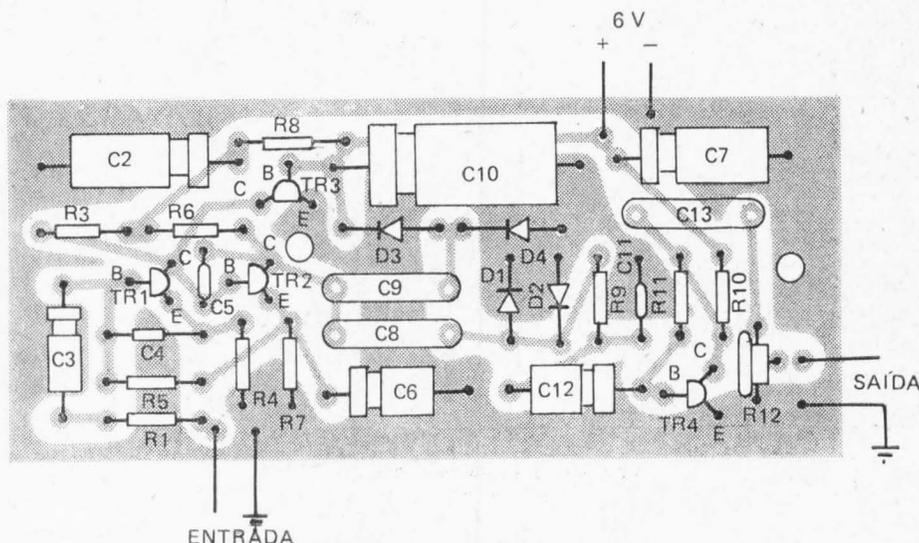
Disposição dos componentes sobre a plaqueta da Fig. 2.
